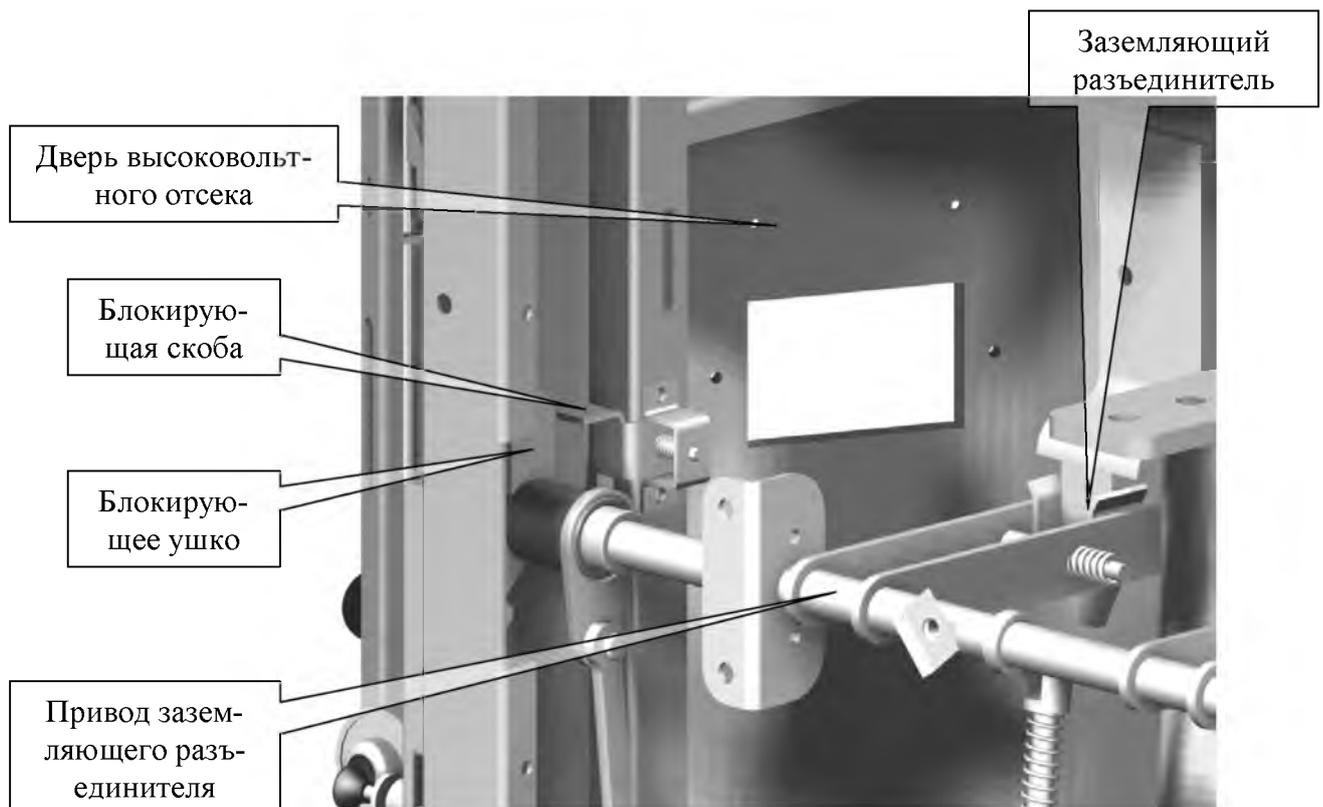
Блокировка двери высоковольтного отсека и заземляющего разъединителя (дверь открыта, заземляющий разъединитель включен).
